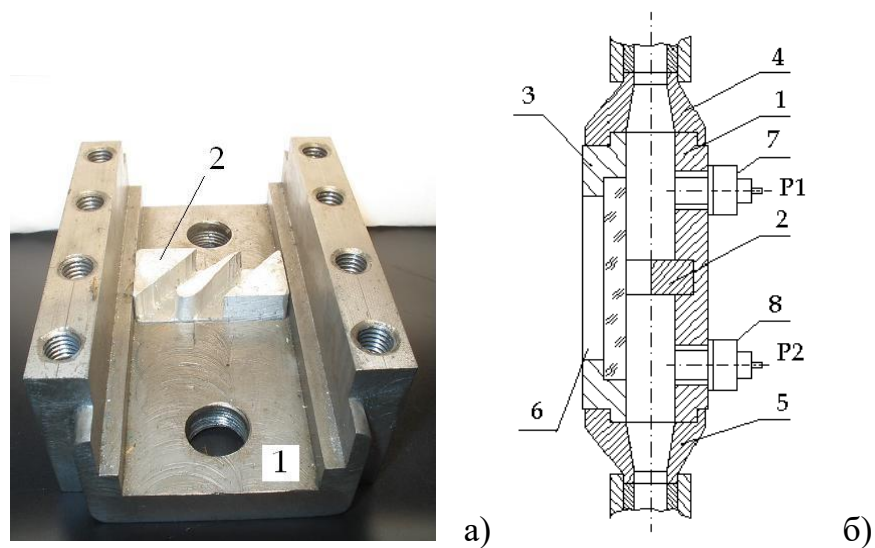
Устройство для визуальных исследований процесса ОАП: а) корпус с образцом; б) схема устройства [7]
